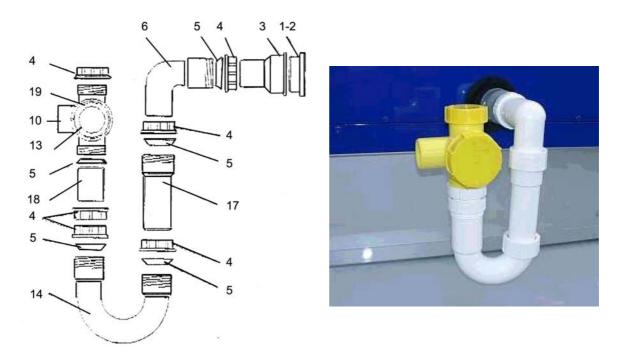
Сифоны типа 100400, 100500, 100600
